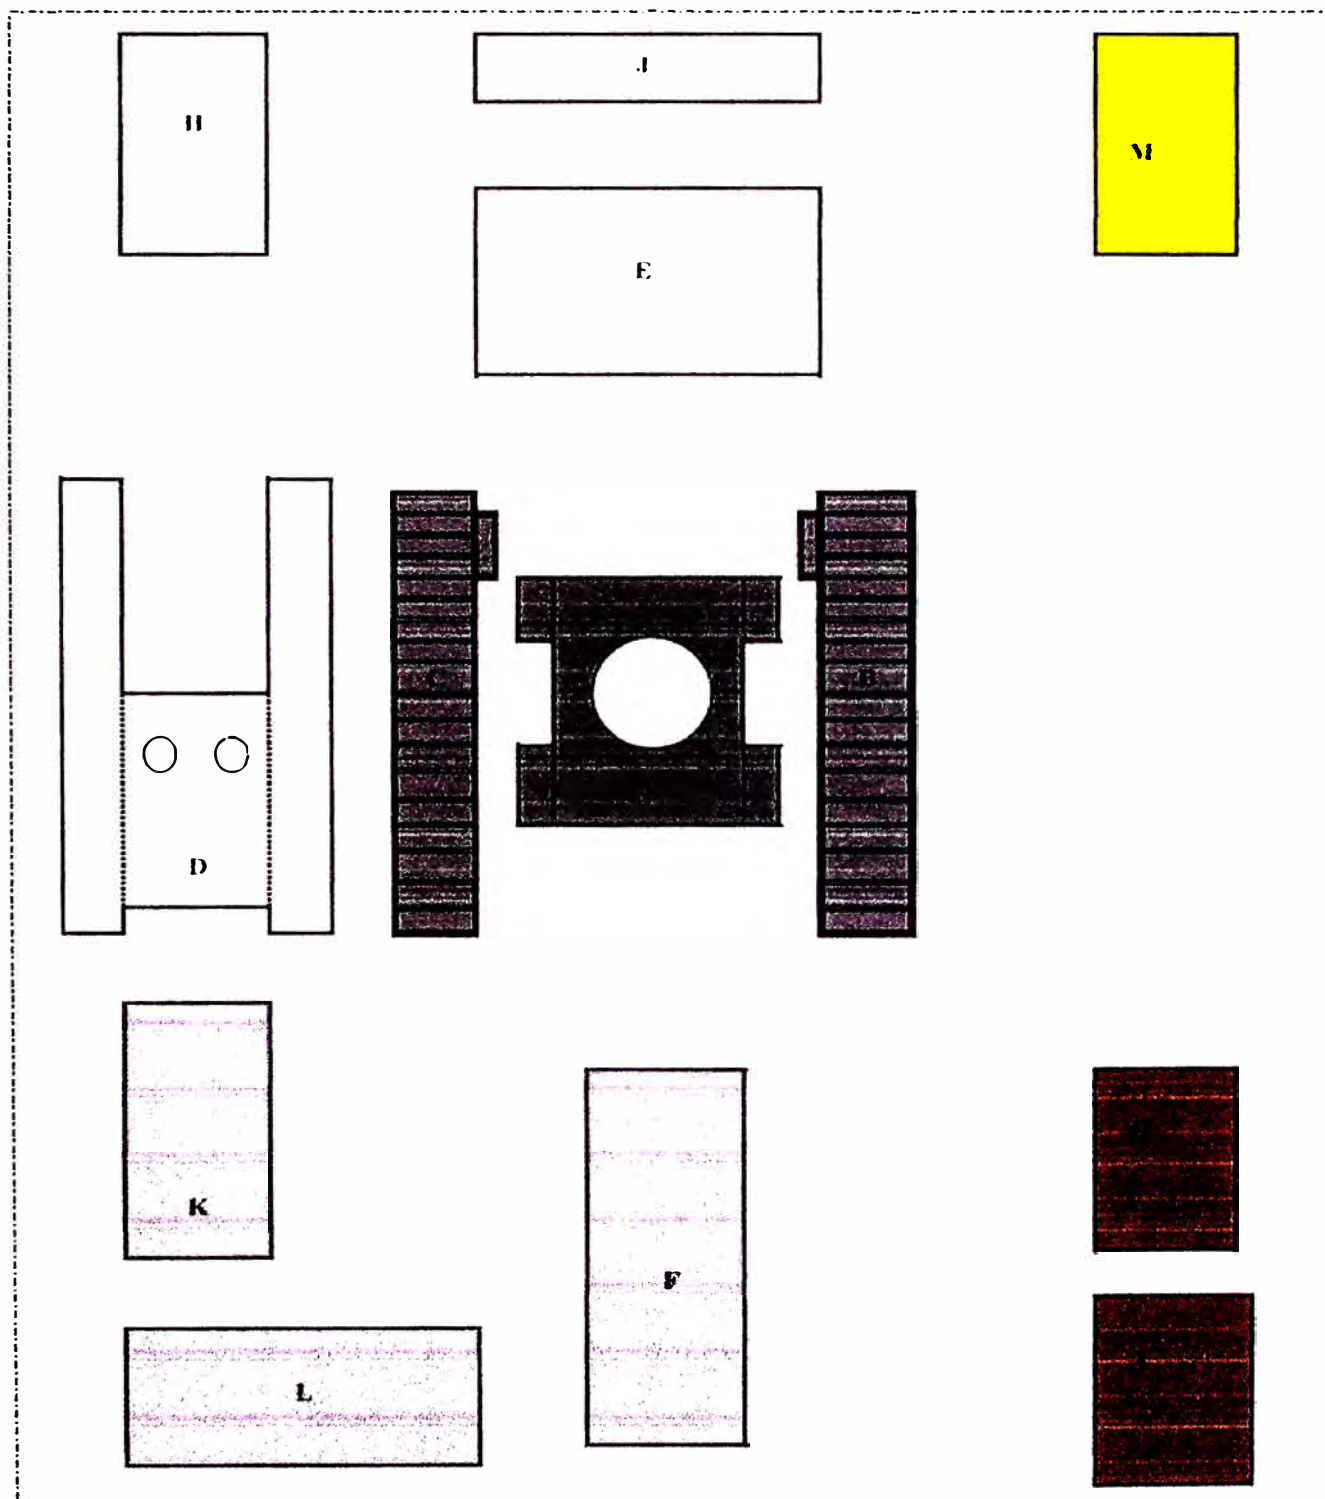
Distribución de Módulos, Componentes y Accesorios sobre el Área de Montaje
